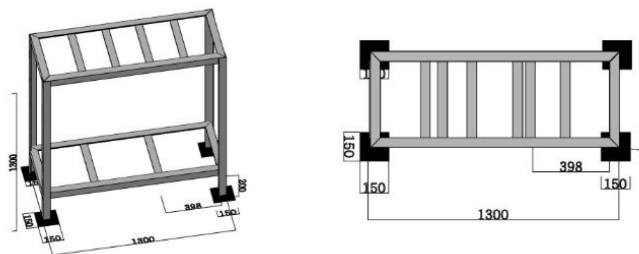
Diseño de la mesa de acero inoxidable 304 para sostener el equipo CIMEL, las medidas están en milímetros)
